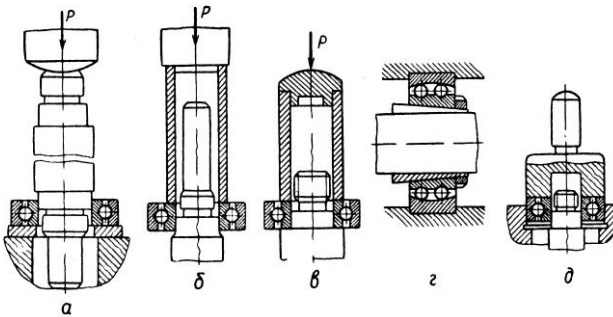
Встановлення підшипників кочення на вал і корпус деталі з використанням : а – підкладного кільця; б, в – монтажної труби; г – гайки; д – оправки
